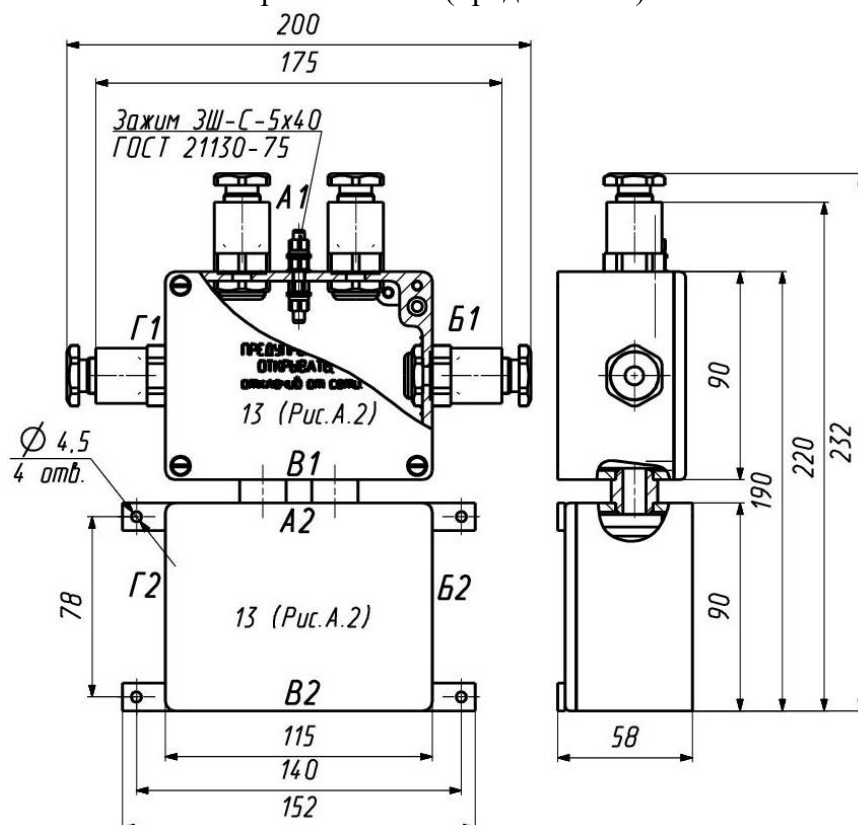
Блок корпусов и коробка клеммная ЕхБКР-А13В1/А13А2 (скрепление двух корпусов типоразмера 13 сторонами В1 и А2) – вариант 7
